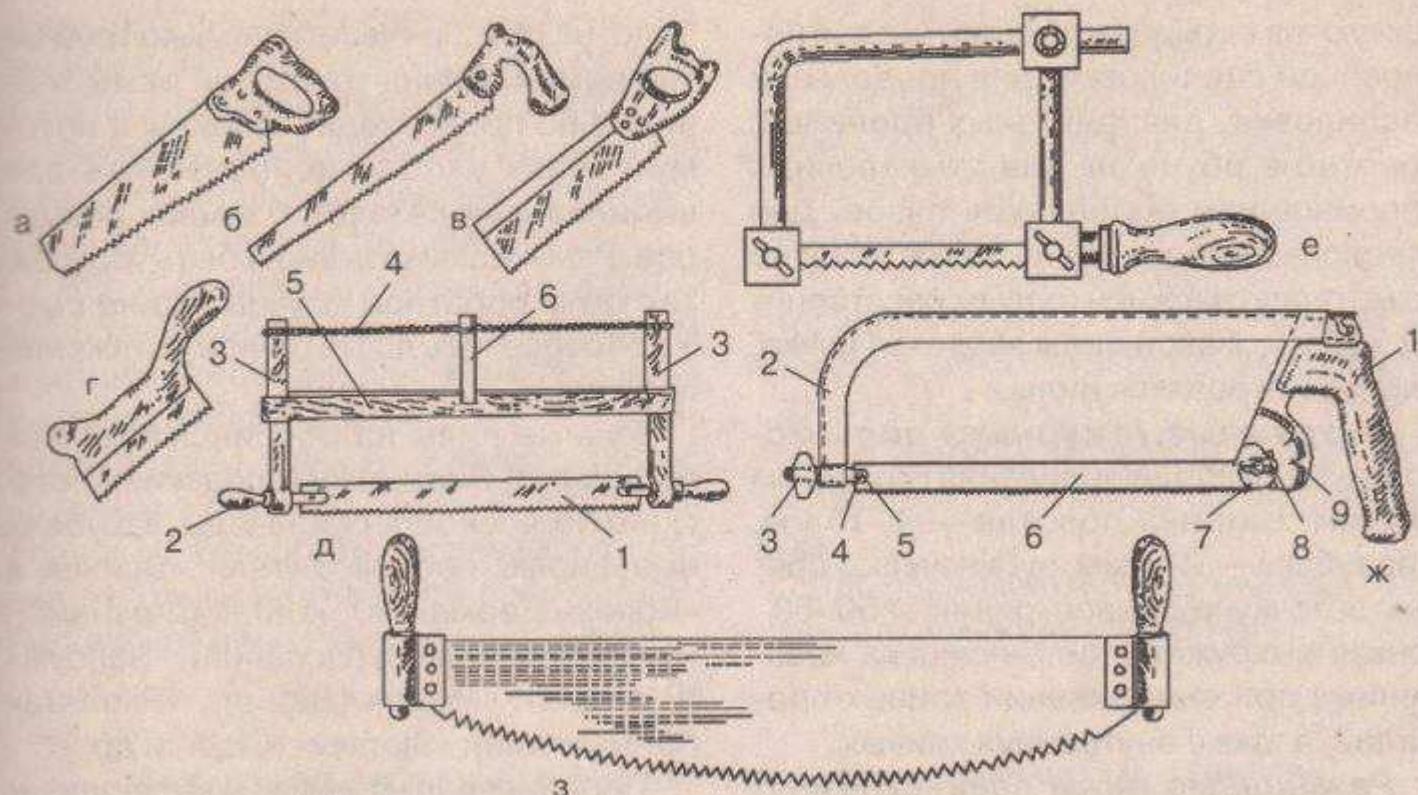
Инструмент для ручного пиления: а — поперечная ножовка (широкая); б — узкая ножовка; в — ножовка с обушком; г — ножовка-наградка; д — лучковая пила; 1 — полотно; 2 — ручка; 3 — стойки; 4 — тетива; 5 — средник; 6 — закрутка; е — лобзик; ж — ножовка универсальная; 1 — ручка; 2 — стальное колено; 3, 8 — гайки; 4 — держатель; 5 — штыри; 6 — полотно; 7 — шайба; 9 — зубчатое зацепление; з — пила поперечная двуручная
